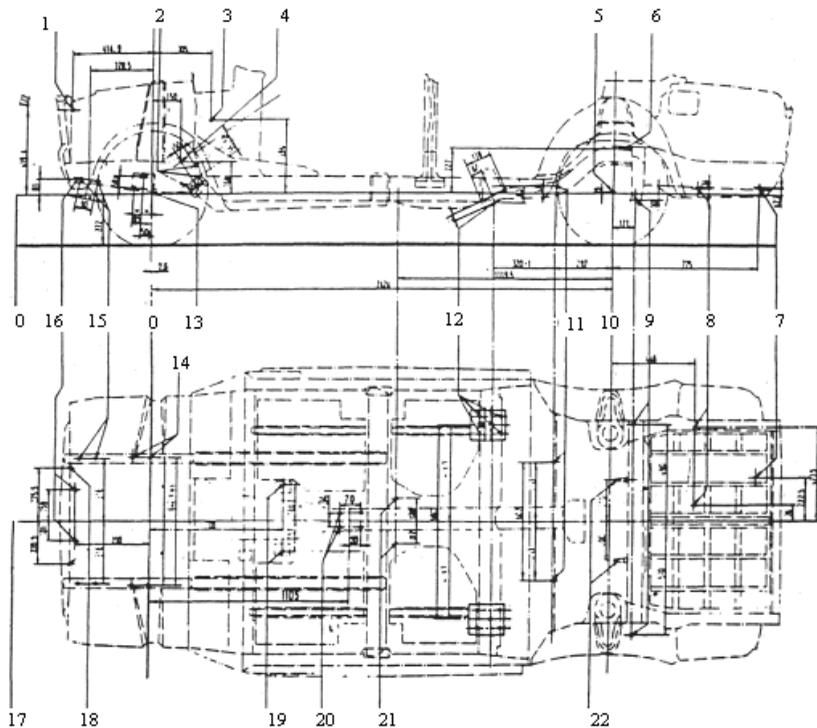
Точки крепления узлов шасси: 0-базовая линия; 1-верхнее крепление радиатора; 2-крепление картера рулевого механизма и маятникового рычага; 3-ось педалей тормоза и сцепления; 4-центр рулевого механизма; 5-центр заднего колеса; 6-крепление амортизатора задней подвески; 7-заднее крепление глушителя; 8-переднее крепление глушителя; 9-крепление поперечной штанги задней подвески; 10-ось задних колёс; 11-крепление верхних продольных штанг задней подвески; 12-крепление нижних продольных штанг задней подвески; 13-центр переднего колеса; 14-точки крепления поперечины передней подвески; 15-крепление стабилизатора поперечной устойчивости; 16-нижнее крепление радиатора; 17-ось автомобиля; 18-верхнее крепление радиатора; 19-заднее крепление силового агрегата; 20-крепление ручного тормоза; 21-крепление опоры карданного вала; 22-крепление амортизатора задней подвески
